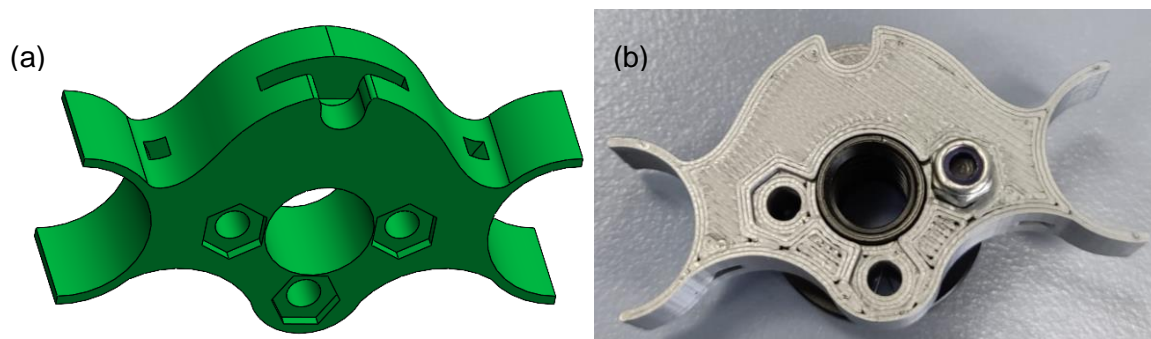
Pieza de acoplamiento entre tuerca y émbolo; (a) Modelo 3D, (b) Pieza impresa en PLA y parcialmente ensamblada.
